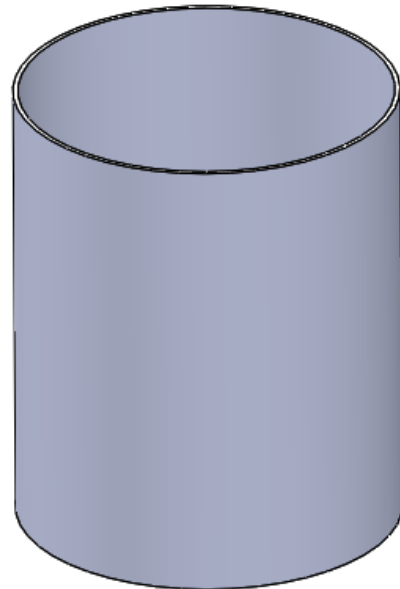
Diseño estructural pieza 1.2 Cilindro interior
